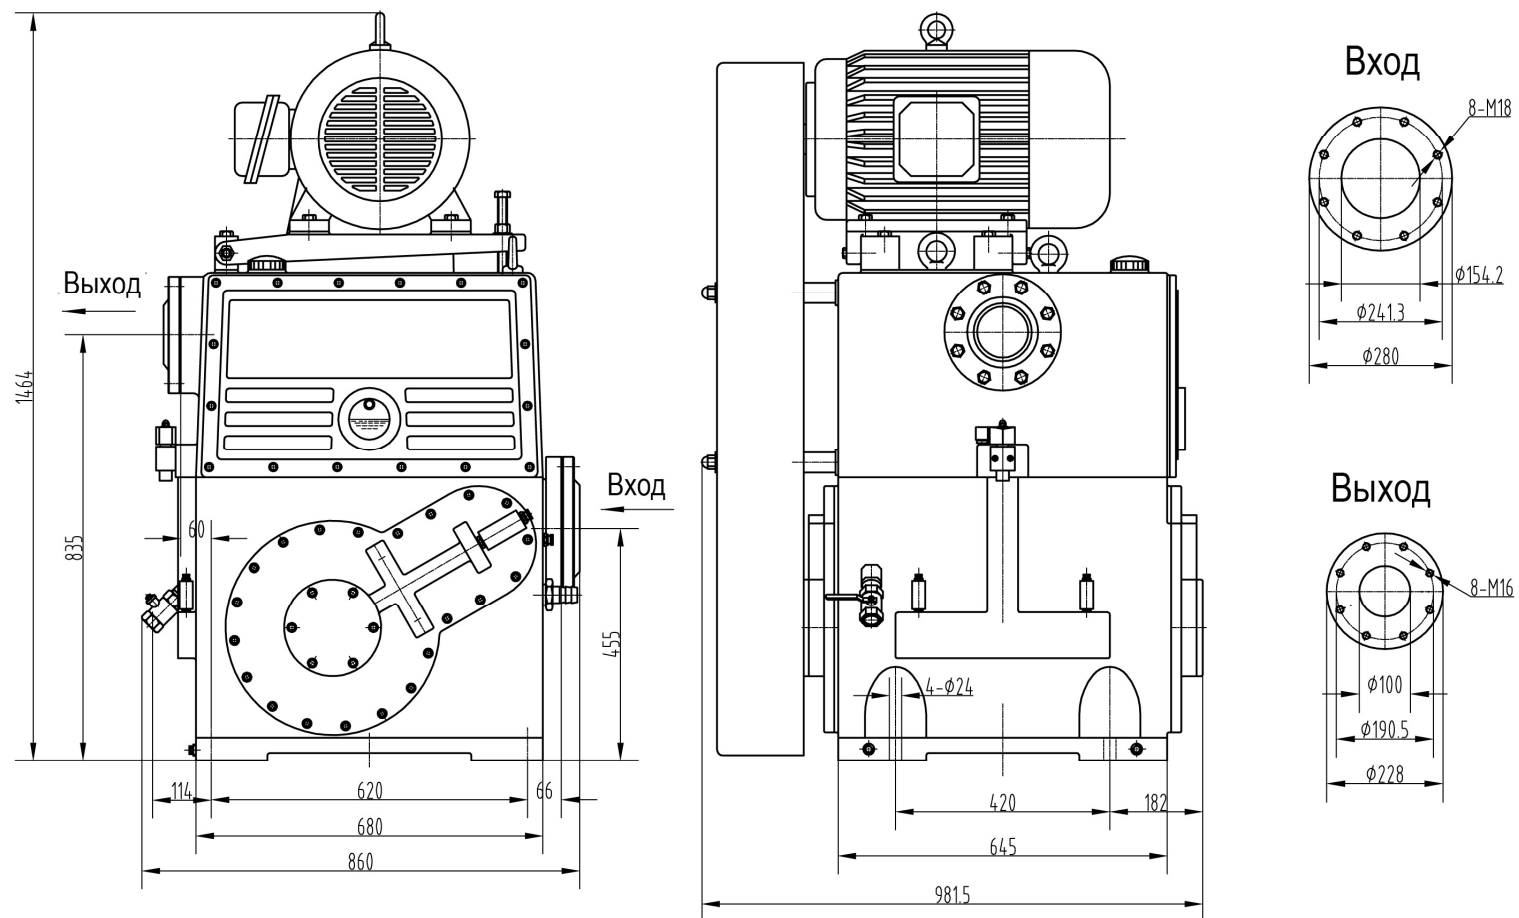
АВПЗ-300 Агрегат вакуумный плунжерный
